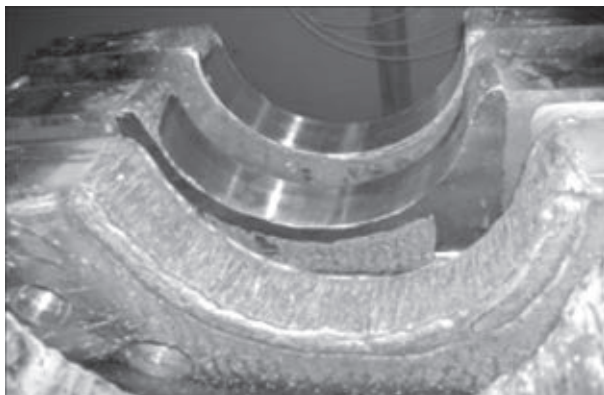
Многослойная наплавка лопасти ножа для горячей резки
